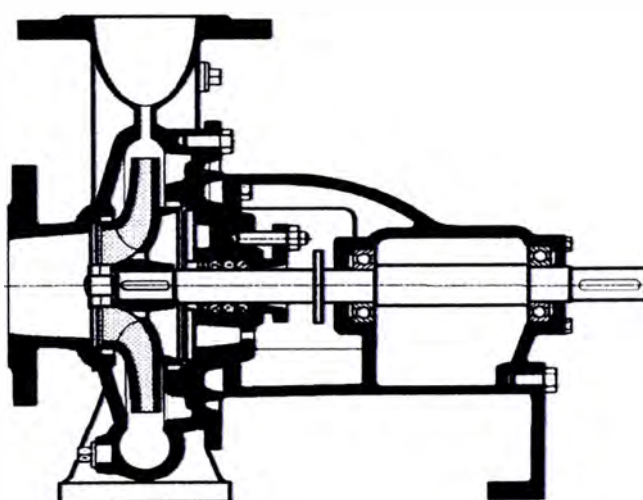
Configuración de una bomba centrífuga con rodajes
